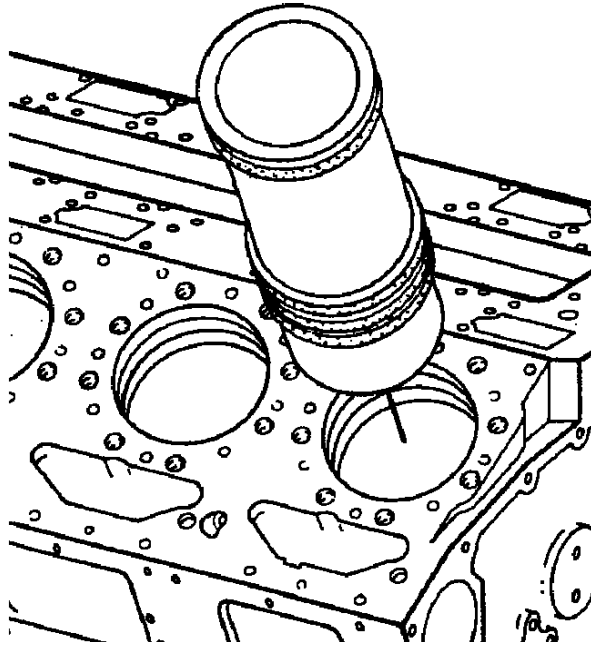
Установка втулки цилиндра двигателя CAT 3516 у блок
